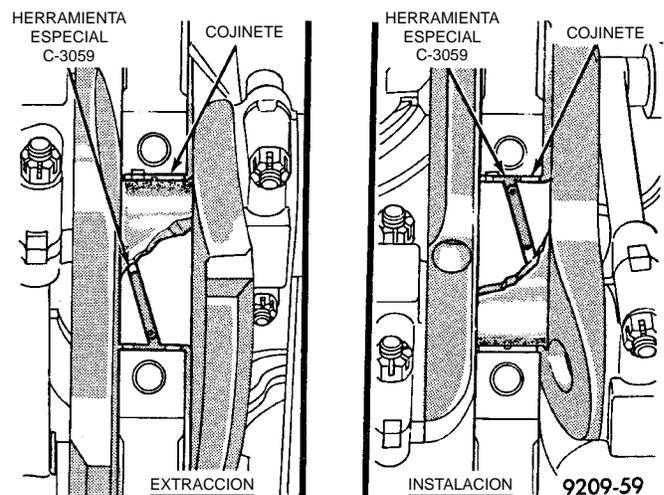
Desmontaje e instalación del cojinete principal superior con la Herramienta C-3059
